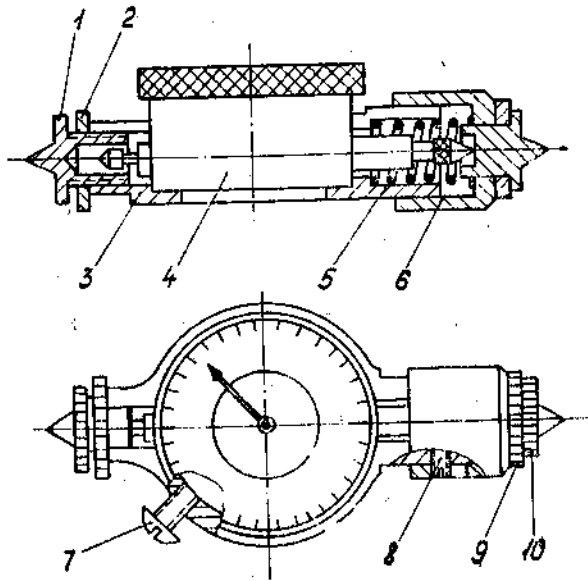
Приспособление для измерения расхождения щек кривошипов коленчатого вала:
